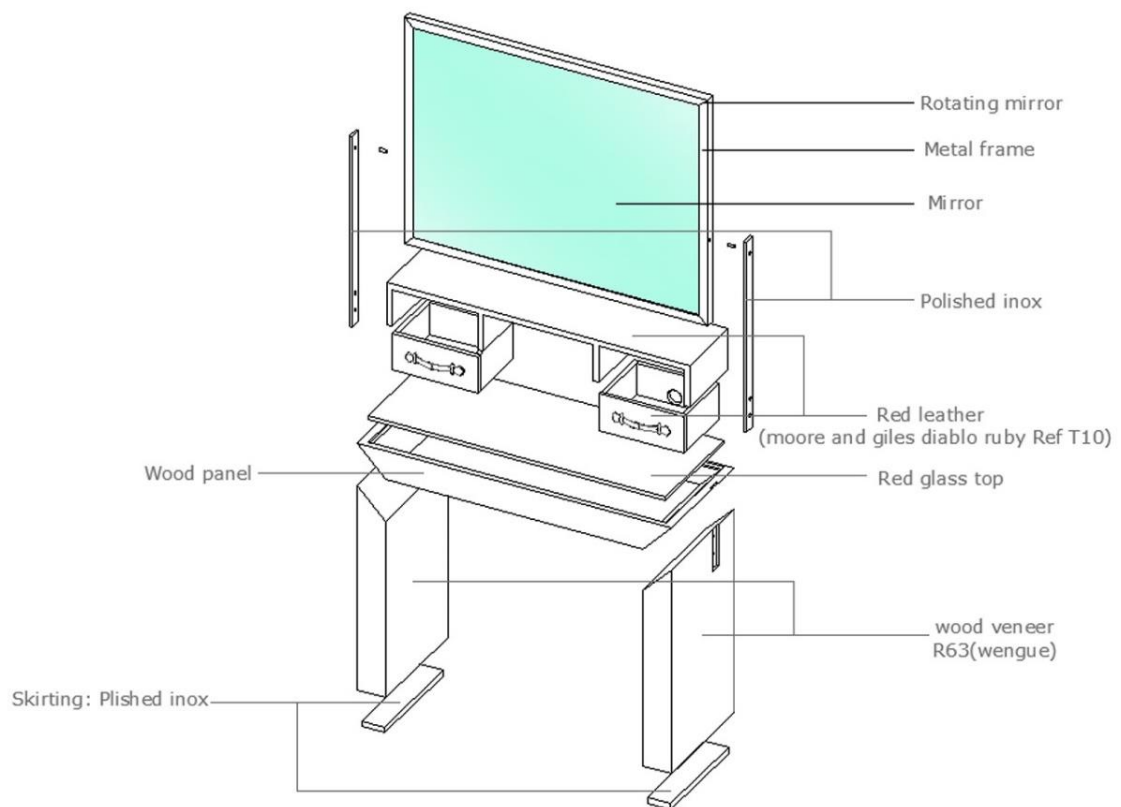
Desenho técnico representativo da construção, gerado através da modelação tridimensional por partes e vistas explodidas.
